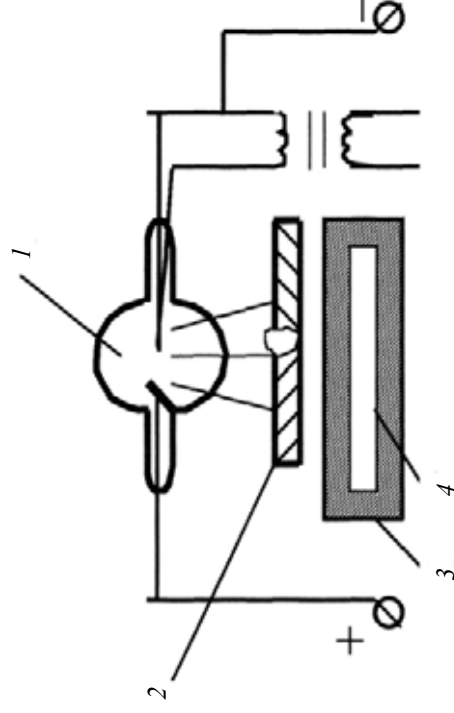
Рентгенографический контроль сварных соединений:
